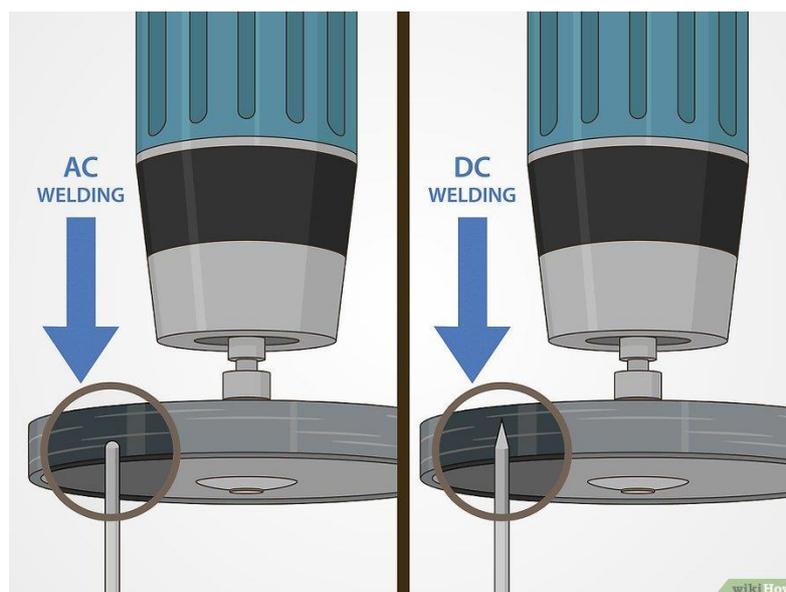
Afilado del electrodo de Tungsteno (Fuente: Wikihow.com)
